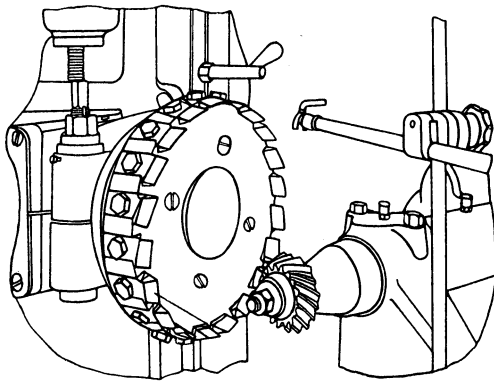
Gleason-Spiralzahnkegelradfräsmaschine.
